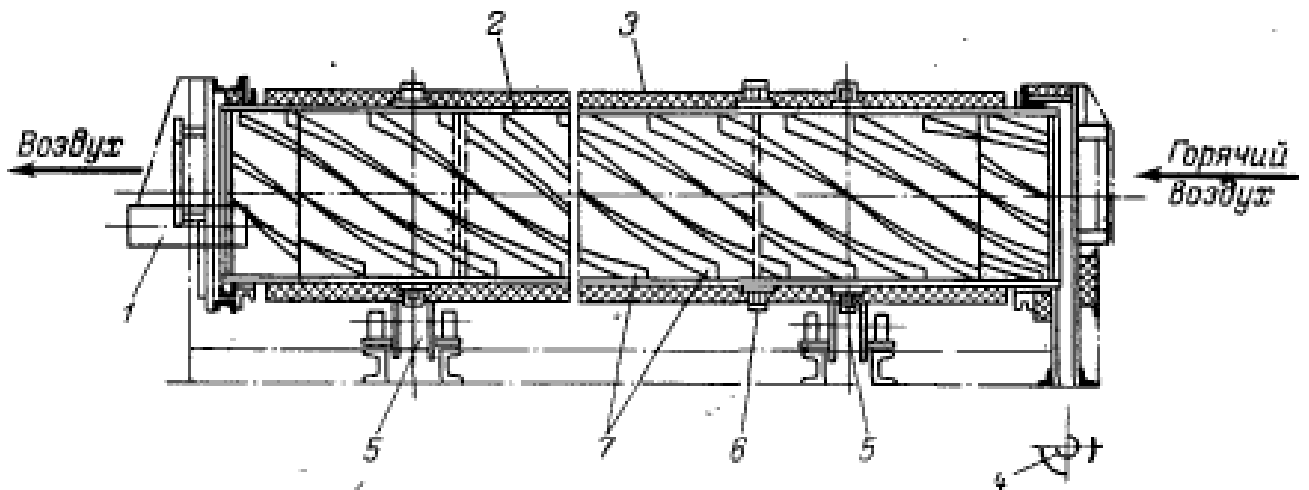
Загальний вигляд барабанної сушарки: 1 – живильник (шнек) для введення вологого бікарбонату натрію в сушарку; 2 – барабан; 3 – термоізоляція; 4 – вивантажувальний шнек; 5 – опорно-упорні ролики; 6 – приводна (венцова) шестерня; 7 – насадка
